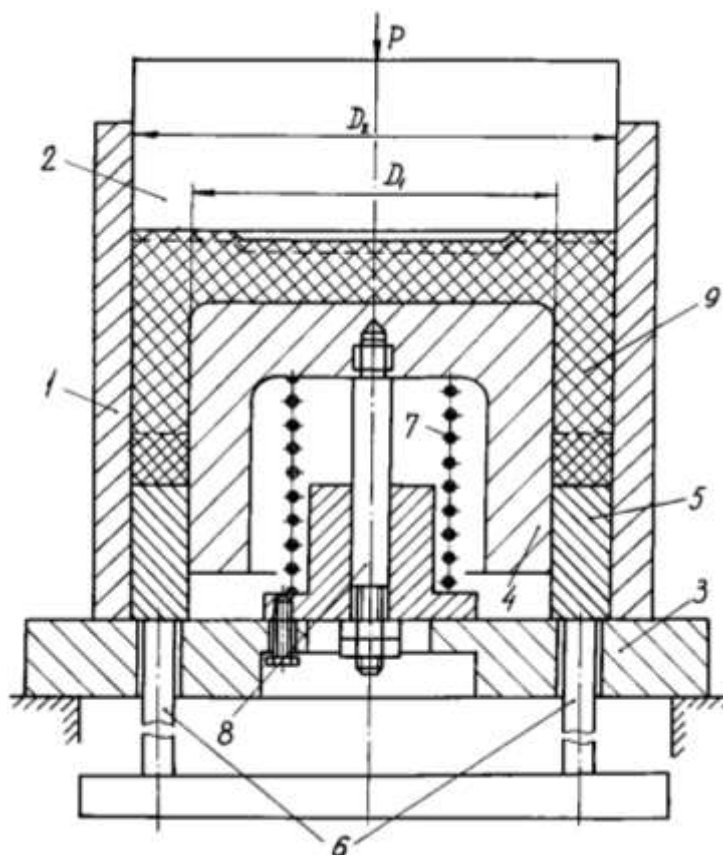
Конструктивна схема прес-форми з нероз'ємною матрицею для виробництва заготовок виробів типу „Капсель”
